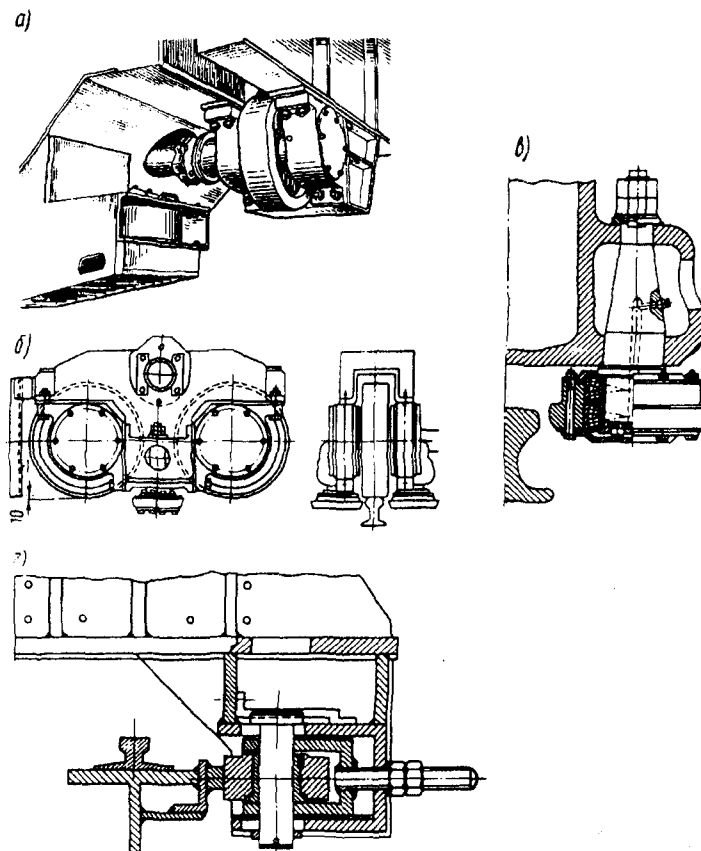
Установка безребордных ходовых колес с направляющими роликами:
